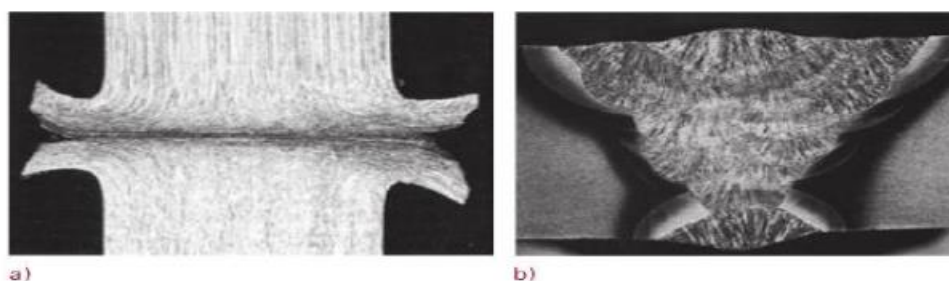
a) Soldadura no estado sólido; b) Soldadura por fusão. (Modenesi, 2012)
